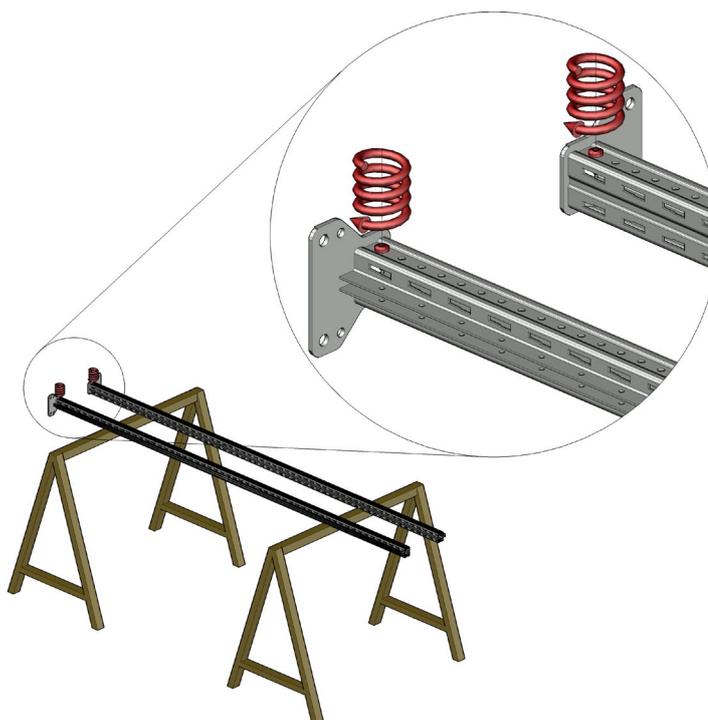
Montage der Fußplatten mit selbstfurchenden Schrauben – Schrauben festdrehen
